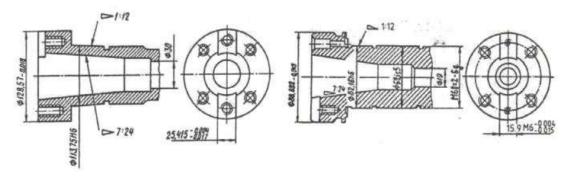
Посадочные и присоединительные размеры конца горизонтального шпинделя
